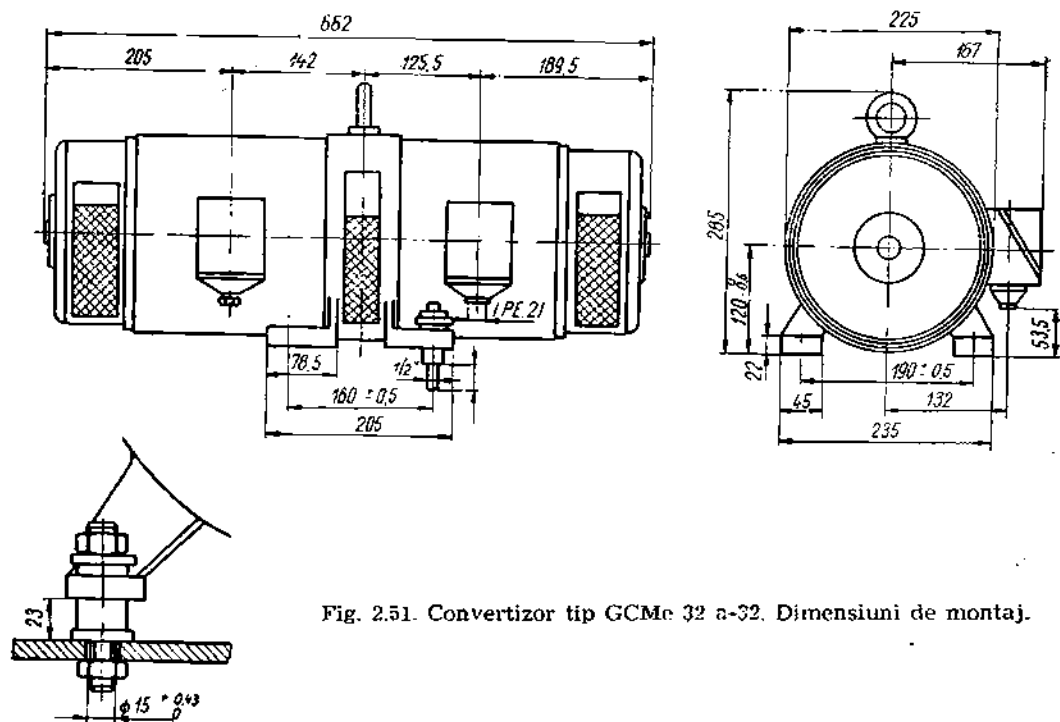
Convertizor tip GCMc 32 a-32. Dimensiuni de montaj.
